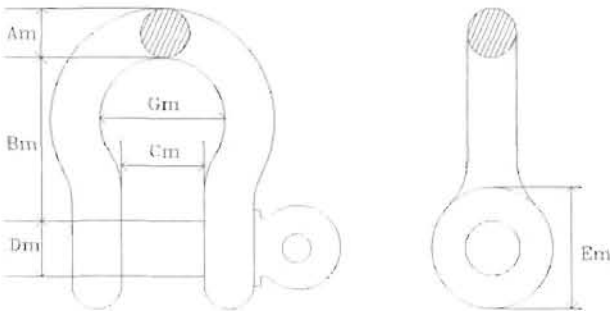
Manille. Vue de face et de profil, et principales dimensions d'une manille.
